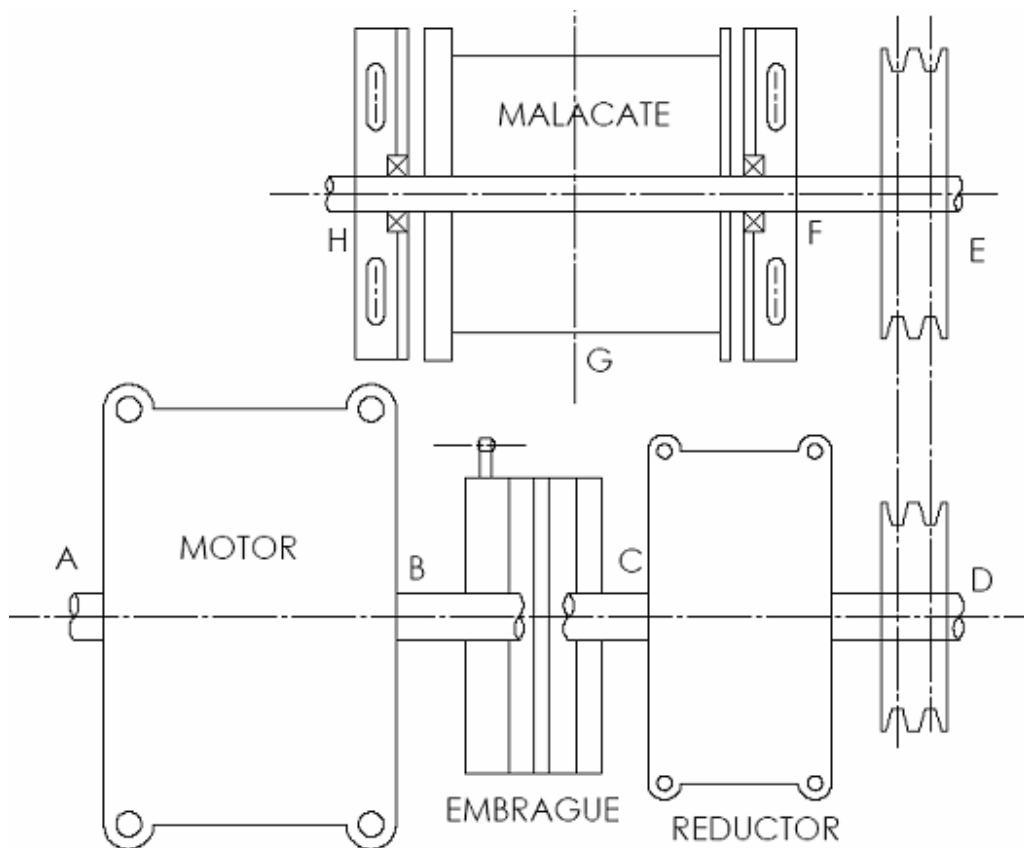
Vista de planta de la máquina con su nomenclatura<sup>[4]</sup>
